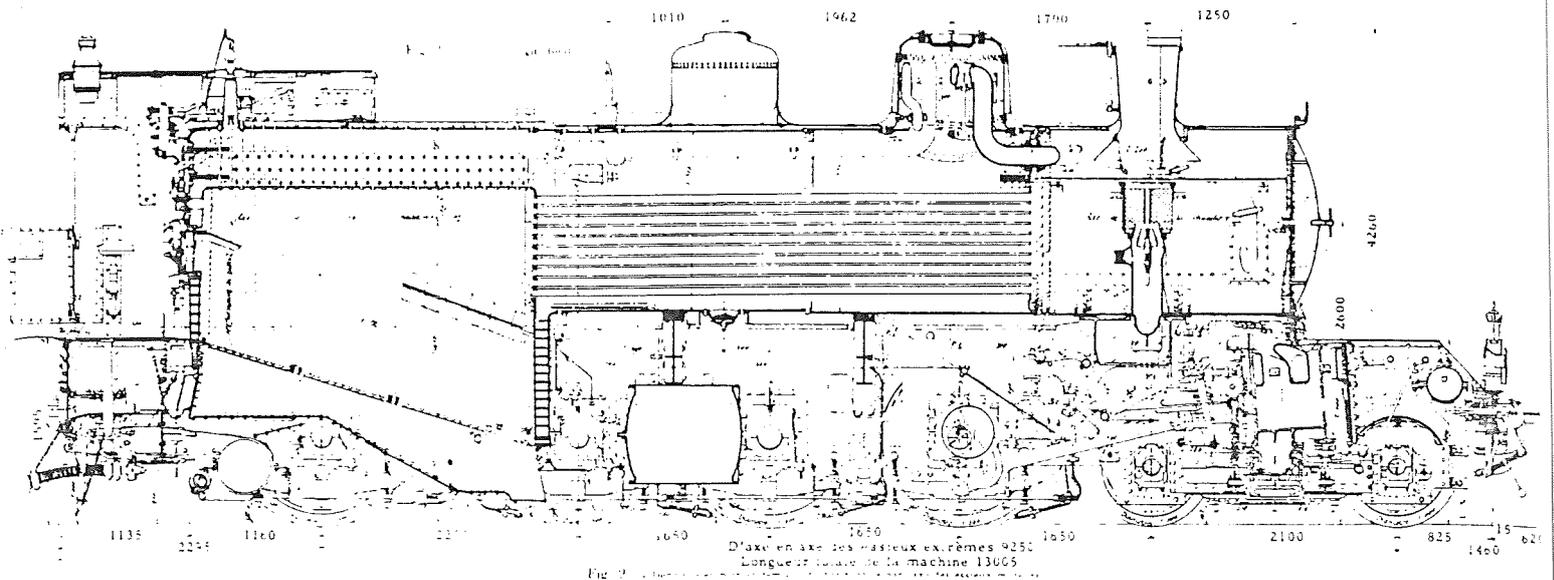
Locomotives 240 A. Coupe longitudinale avant application d'un surchauffeur.
